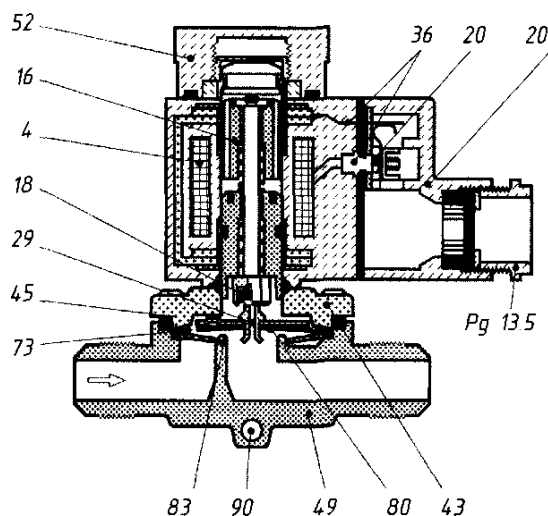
Устройство соленоидного клапана *EVR 10 (NO)*: 4 — обмотки; 13,5 — сальниковый ввод; 16 — сердечник; 18 — пластина клапана; 20 — заземление; 29 — дюза; 36 — пробка; 43 — крышка клапана; 45 — уплотнение; 49 — корпус клапана; 52 — крышка; 73 — отверстие для уравнивания; 80 — диафрагма; 83 — седло клапана; 90 — монтажное отверстие
